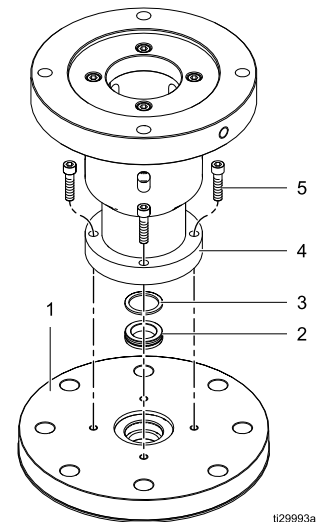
Remplacement du joint de l'arbre pour montage à bride/bride rapide
